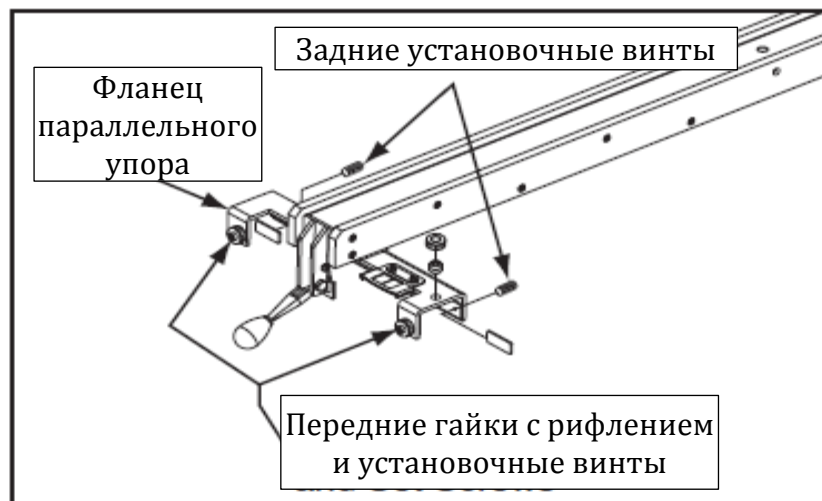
Расположение установочных винтов, служащих для регулировки параллельности параллельного упора и усилия прижима
